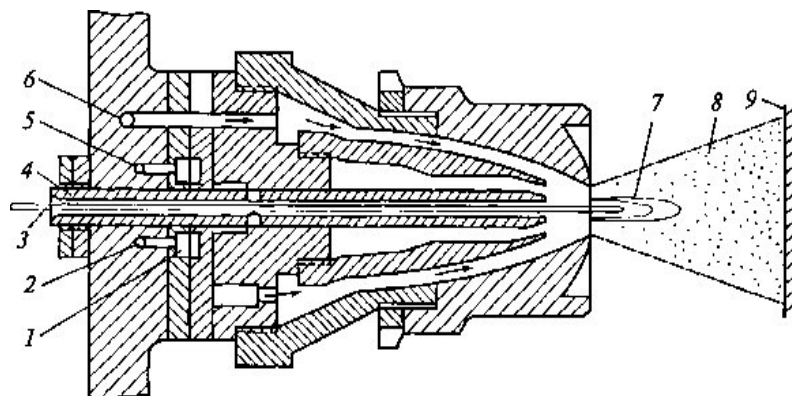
Розпилювальна головка газовогняного дрового апарату для напилювання: 1 - змішувальна камера; 2 - канал підведення кисню; 3 - дріт; 4 - напрямна втулка; 5 - канал підведення ацетилену; 6 - повітряний канал; 7- ацетиленокисневе полум'я; 8- газометалічний струмінь; 9- напилювана поверхня деталі
